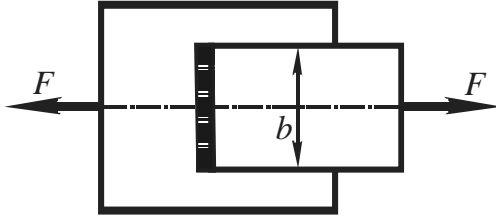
Лобовой сварной шов, нагруженный растягивающей силой
